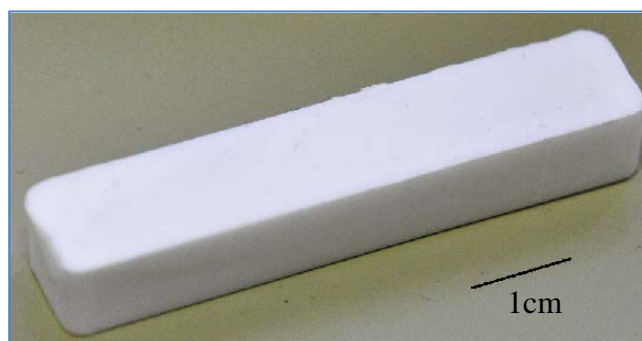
Barreau de PS/PLA mélangé à 190 °C par extrusion jumelée au moulage par injection (sans recuit).
